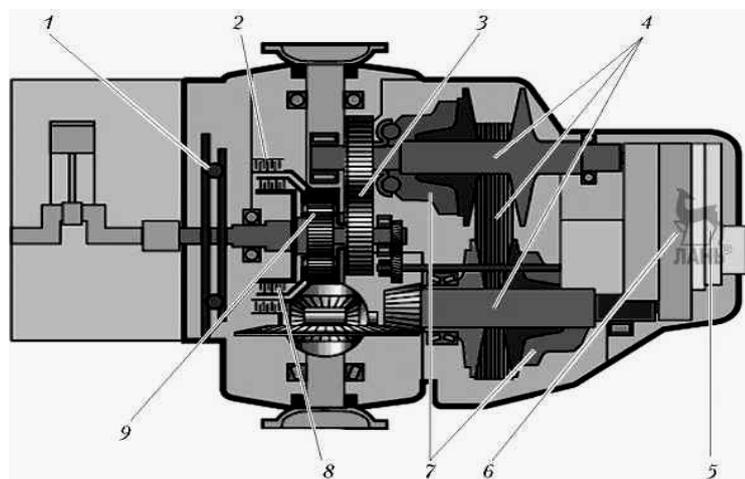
Схема бесступенчатой коробки передач автомобиля Audi: 1 — маховик с встроенным демпфером; 2 — фрикционы для движения задним ходом; 3 — промежуточная передача; 4 — вариатор с цепью; 5 — электронный блок управления коробкой; 6 — гидравлическое управляющее устройство; 7 — гидравлическая система передвижения вариаторов; 8 — фрикционы для движения передним ходом; 9 — планетарный передаточный механизм.
